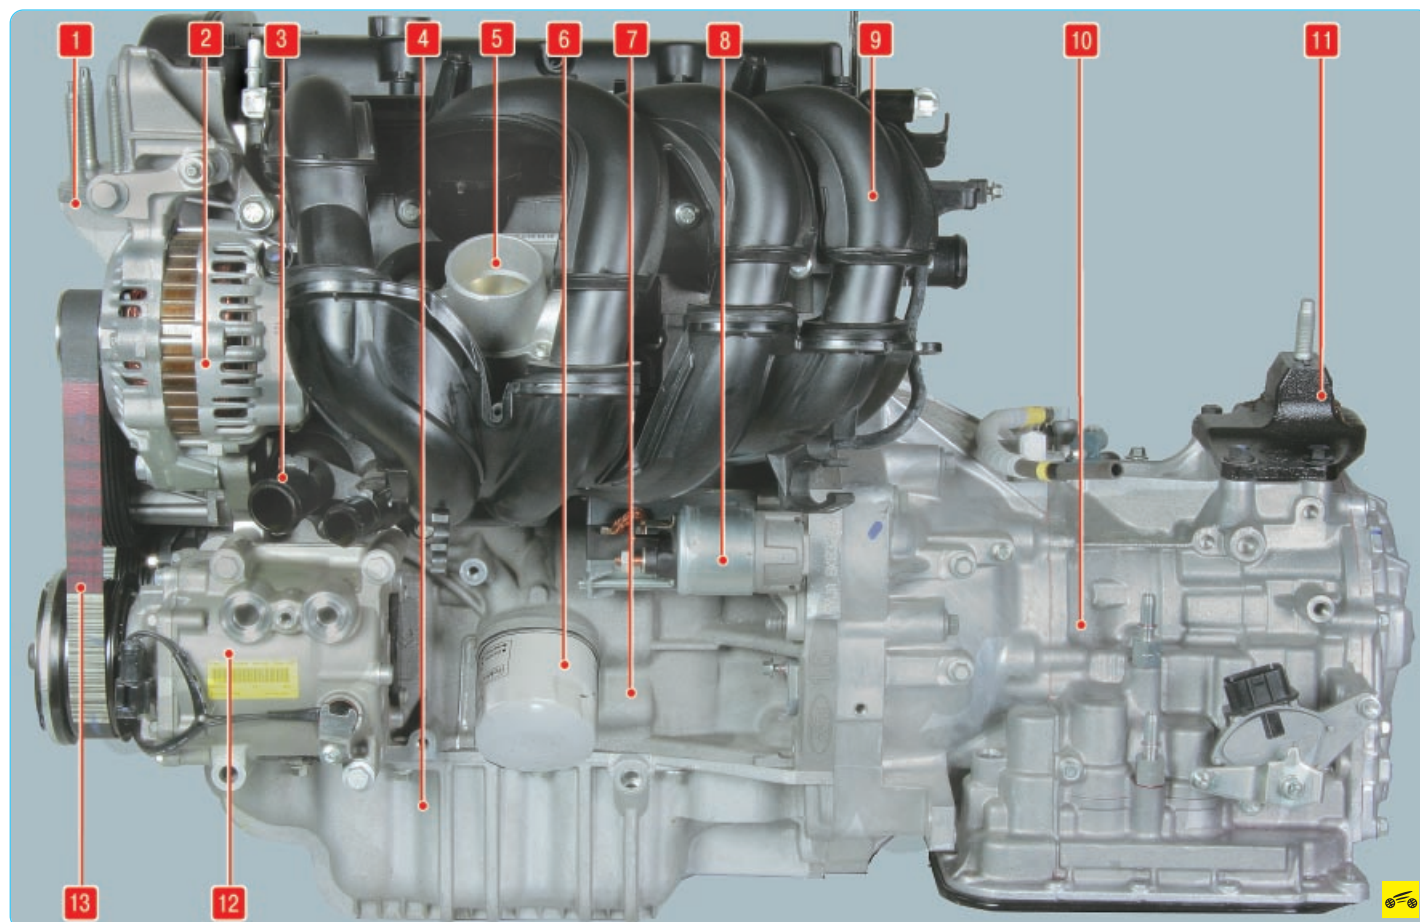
Силовой агрегат Duratec объемом 1,6 л (вид спереди по направлению движения): 1 – кронштейн правой опоры силового агрегата; 2 – генератор; 3 – корпус термостата; 4 – масляный картер; 5 – дроссельный узел; 6 – масляный фильтр; 7 – блок цилиндров; 8 – стартер; 9 – впускной коллектор; 10 – автоматическая коробка передач; 11 – левая опора силового агрегата; 12 – компрессор кондиционера; 13 – ремень привода вспомогательных агрегатов
